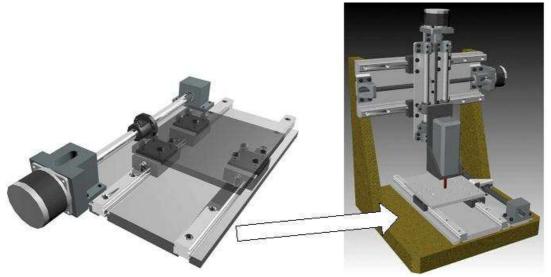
Posicionador Modular para a Máquina CNC de Pequeno Porte (SHOJI, 2002)
